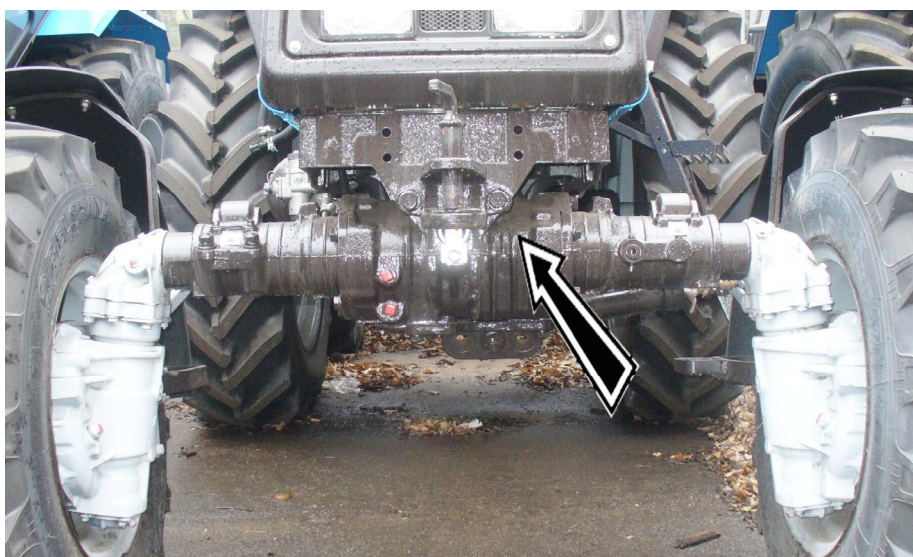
Место расположения номера ПВМ с коническими колесными редукторами
